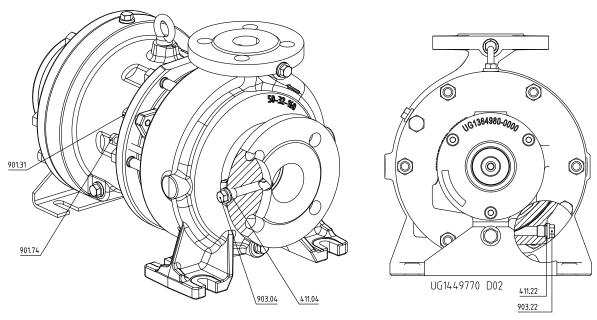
Befestigung Druckdeckel am Pumpengehäuse bei Ausführung mit geklemmtem Deckel Konstruktionsvarianten
